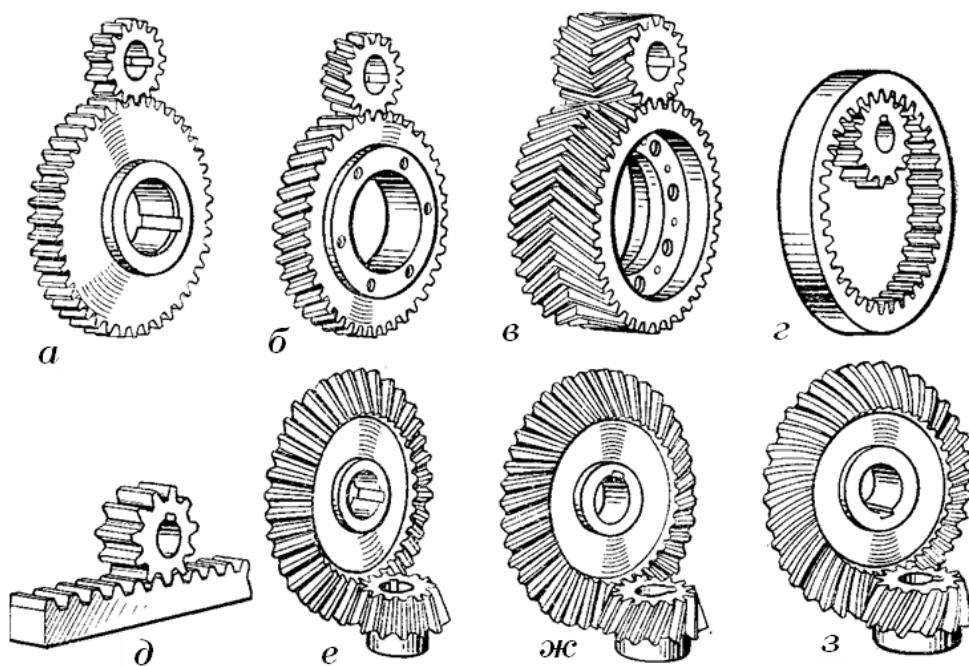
Зубчасті передачі: а - прямозубі; б - косозубі; в - шевронні; г - прямозуба з внутрішнім зачепленням; д - рейкова передача; е - конічна передача з прямим зубом; ж - конічна передача з косим зубом; з - конічна передача з криволінійним зубом
